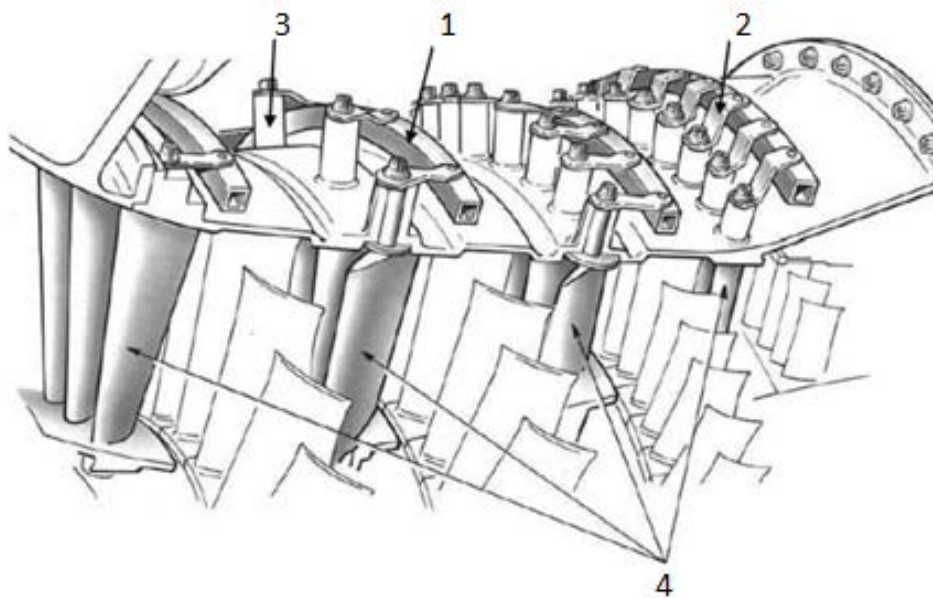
Поворотный направляющий аппарата компрессора в ГТУ
